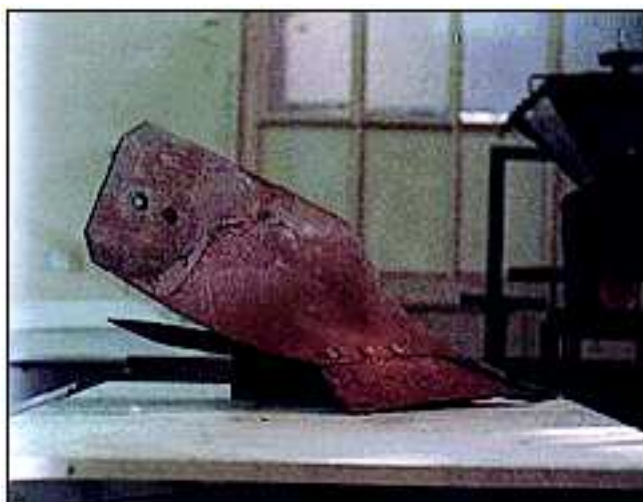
Forme ENPMA (vue latérale YOZ)
